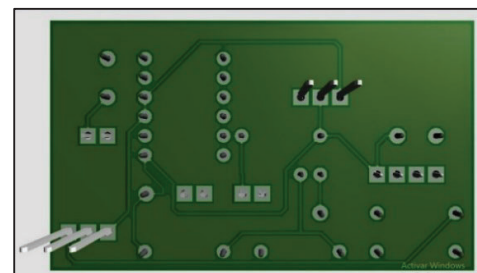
Modelado en 3D de la PCB vista inferior. Fuente: Propia
